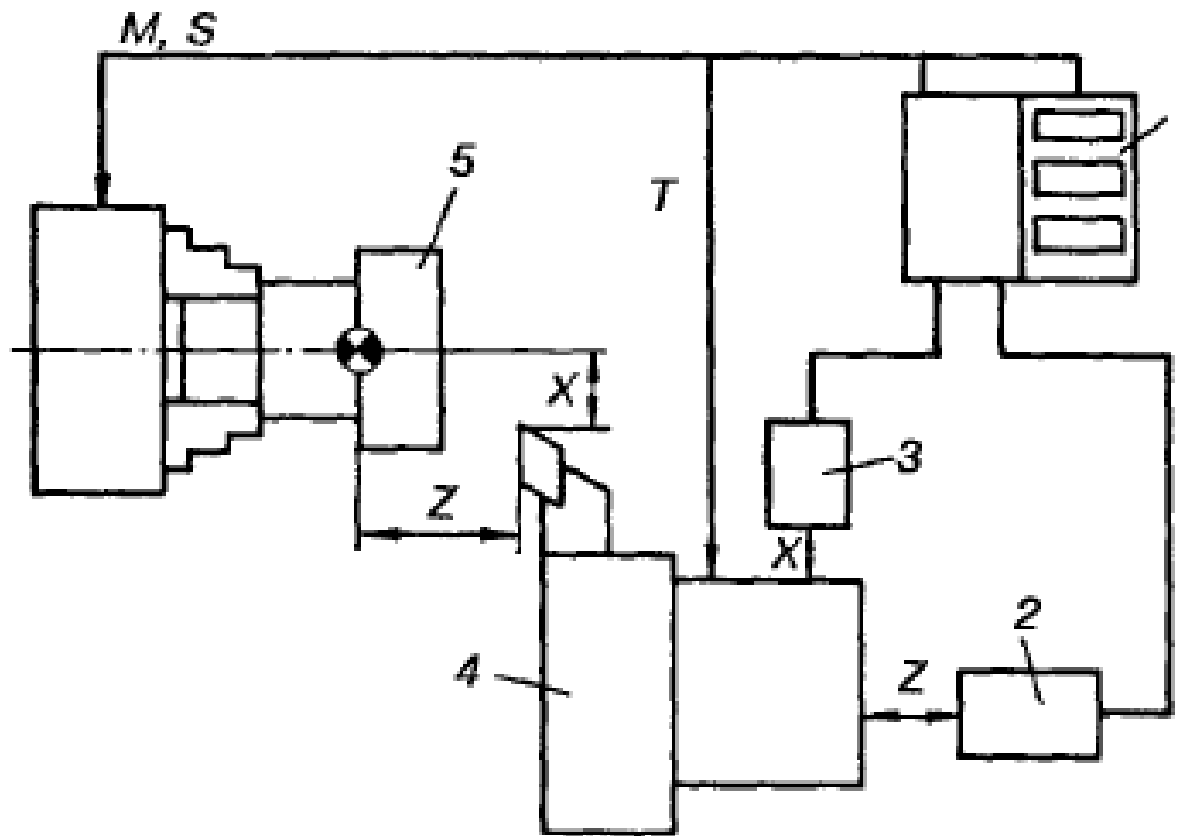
Схема обробки деталі на верстаті 16К20Ф3 з ЧПК
